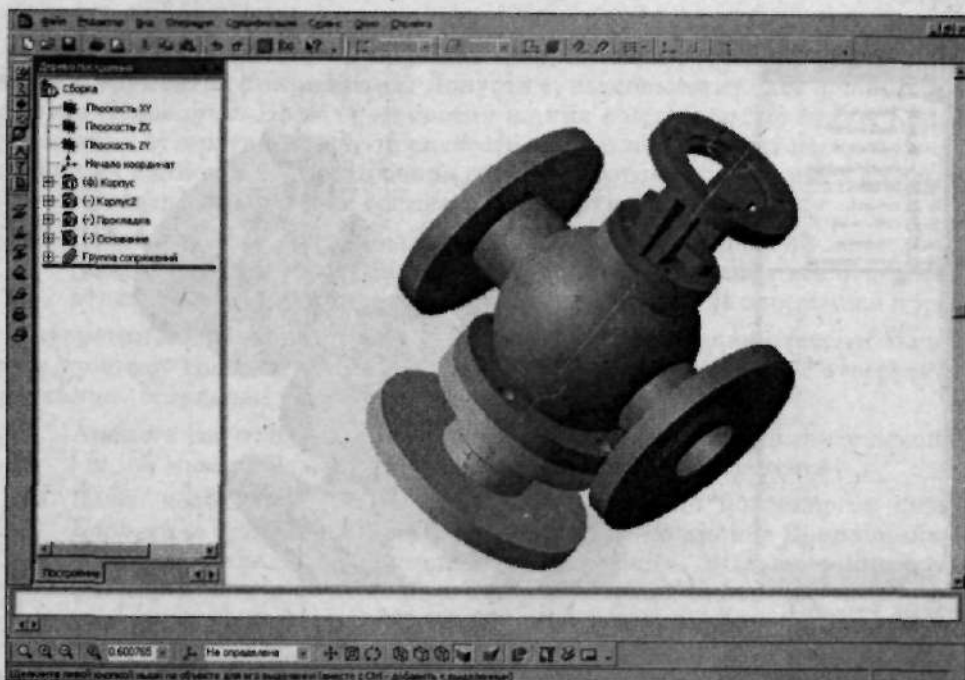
Вид сборки после совмещения детали Корпус и Основание
